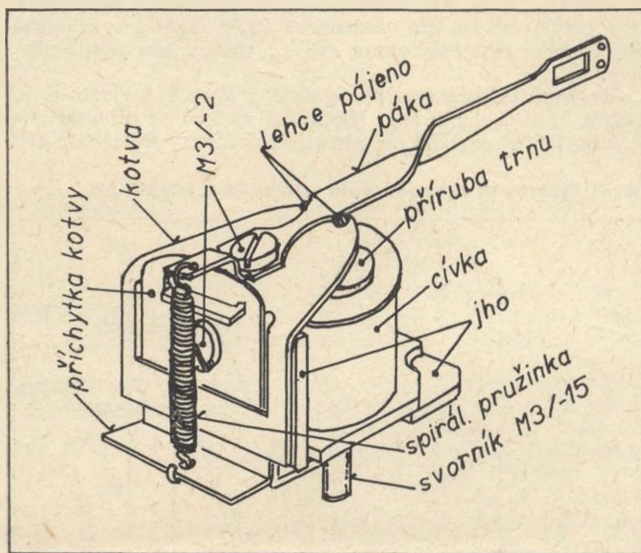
Úprava detailů elektromagnetu z relé HC 100
